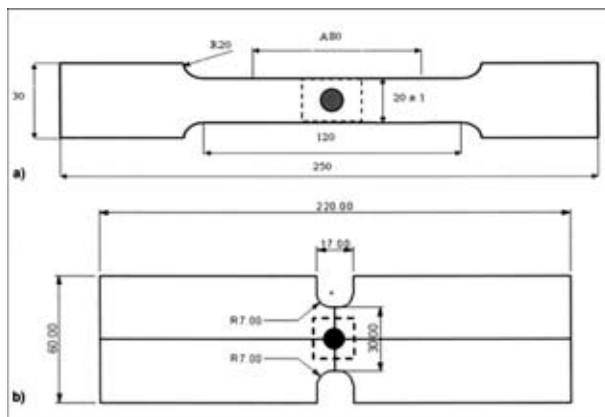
Форма образцов для различных видов испытаний точечного сварного соединения: а — одноосное растяжение; в — двuosное напряжение
